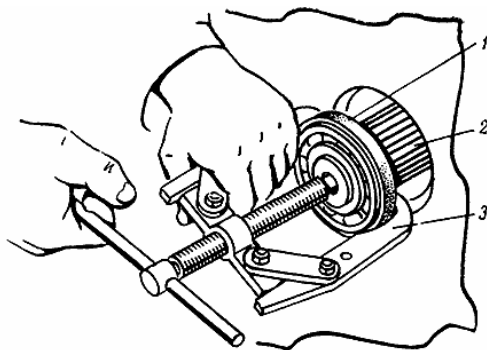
Спрессовка подшипника с вала 1-й передачи и заднего хода:
